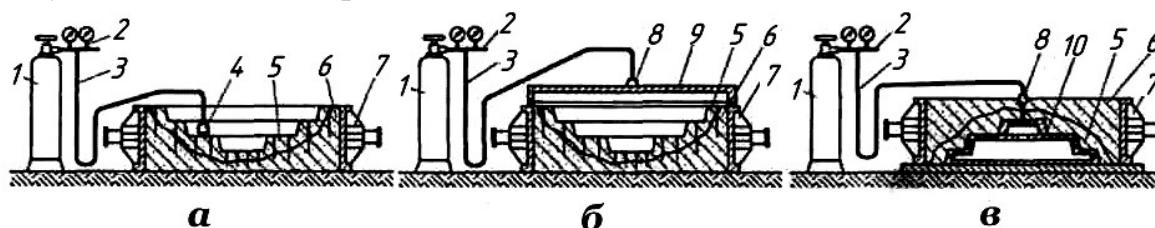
Способы продувки форм углекислым газом: а, б – после удаления модели; в – до удаления модели; 1 – баллон с CO_2 ; 2 – редуктор; 3 – резиновый шланг; 4 – сопло; 5 – химически твердеющая облицовочная смесь; б – наполнительная смесь; 7 – опока; 8 – ниппель; 9 – зонтик; 10 – модель
